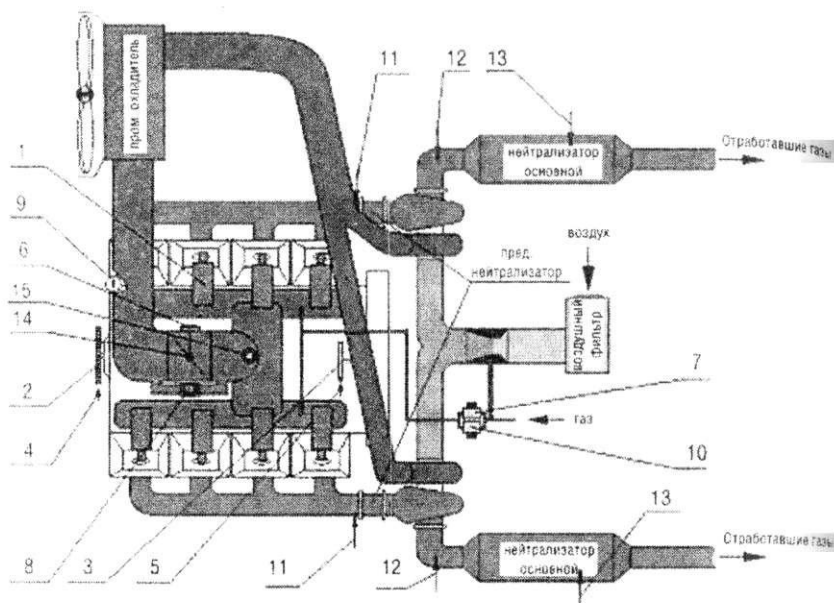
Схема газового двигателя с наддувом и эжекционной подачей газа перед компрессором:
